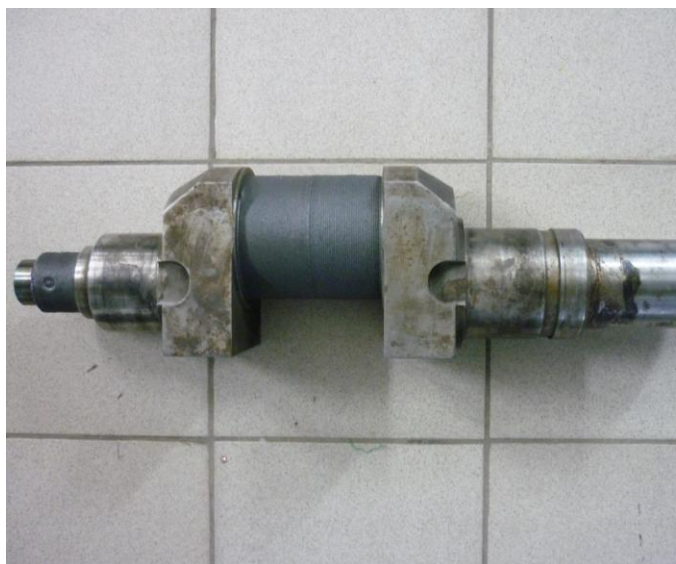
Наплавленная шатунная шейка коленчатого вала.
